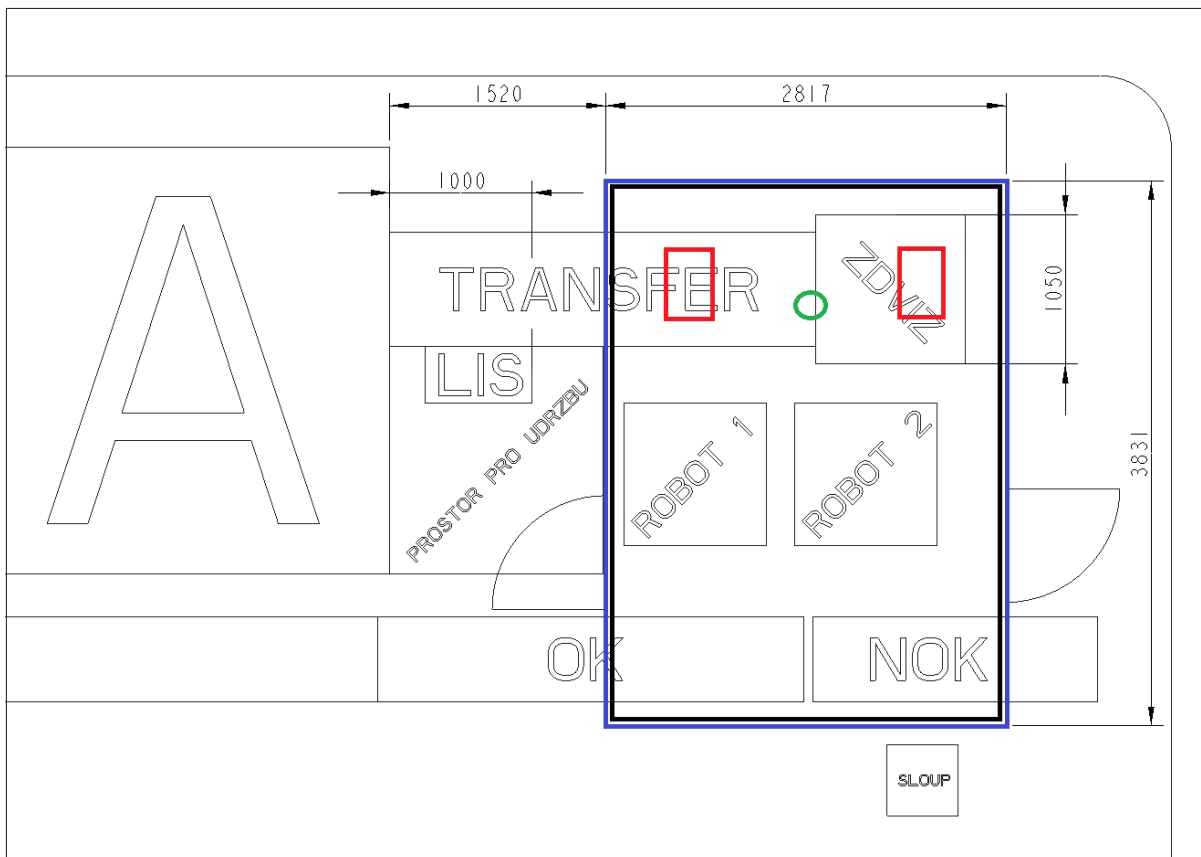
Detail layoutu – otočný stůl s robotickou manipulací [Zdroj: vlastní]
